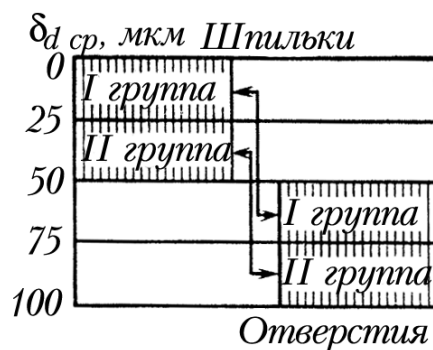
Схема рассортировки шпилек и резьбовых гнезд по среднему диаметру резьбы.
